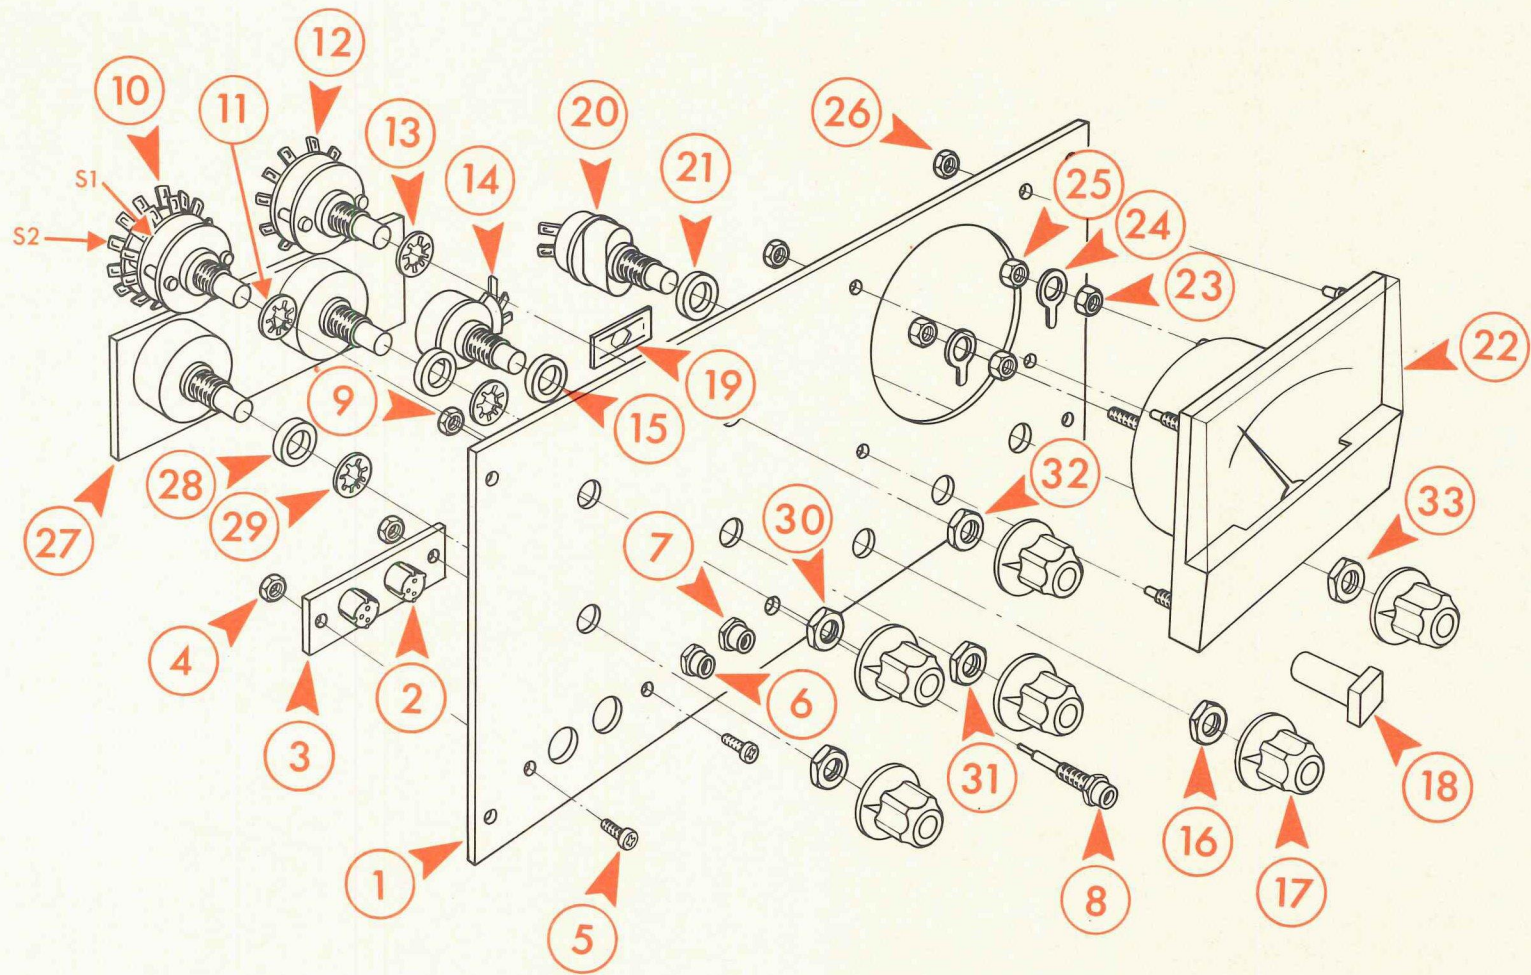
Esploso di montaggio dei componenti sul pannello frontale.
